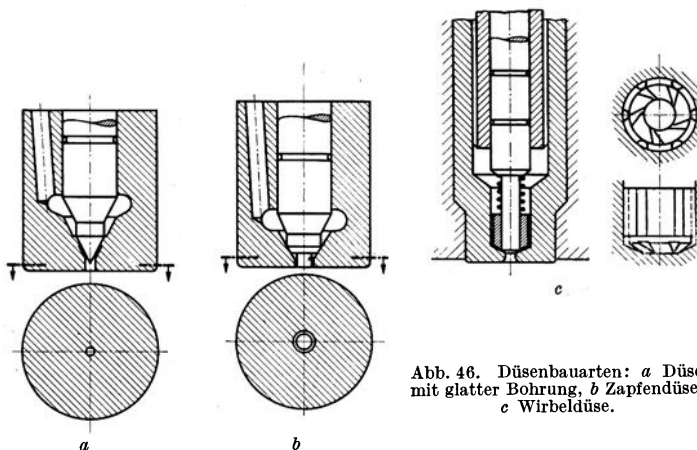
Düsenbauarten: a Düse mit glatter Bohrung, b Zapfendüse, c Wirbeldüse.
